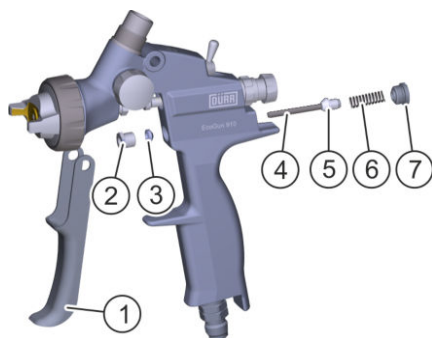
Remplacement du joint de presse-étoupe de vanne
